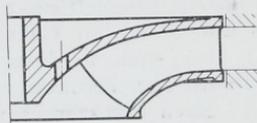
Francisturbine für geringe Laufgeschwindigkeit.
